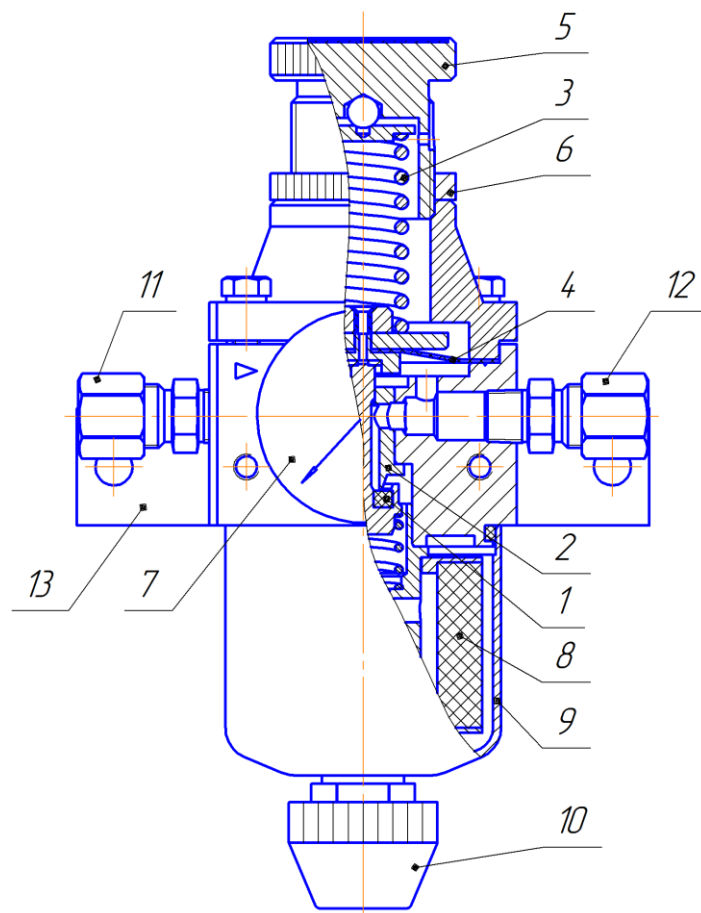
Конструкция редуктора РДФ-01М
